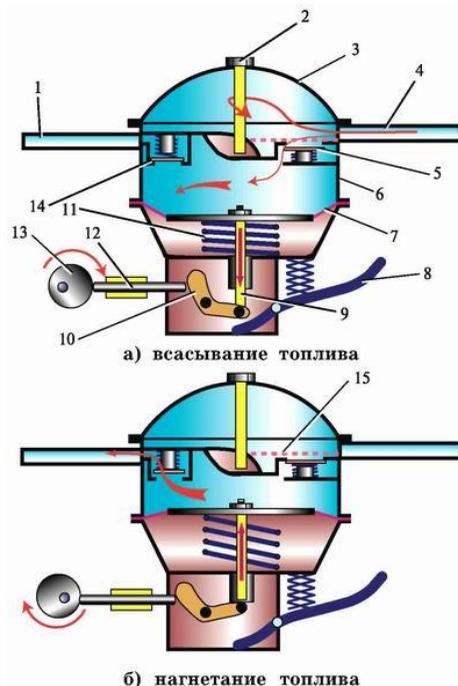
Схема работы топливного насоса: 1 – нагнетательный патрубкок; 2 – стяжной болт; 3 – крышка; 4 – всасывающий патрубкок; 5 – впускной клапан с пружиной; 6 – корпус; 7 – диафрагма насоса; 8 – рычаг ручной подкачки; 9 – тяга; 10 – рычаг механической подкачки; 11 – пружина; 12 – шток; 13 – эксцентрик; 14 – нагнетательный клапан с пружиной; 15 – фильтр очистки топлива
